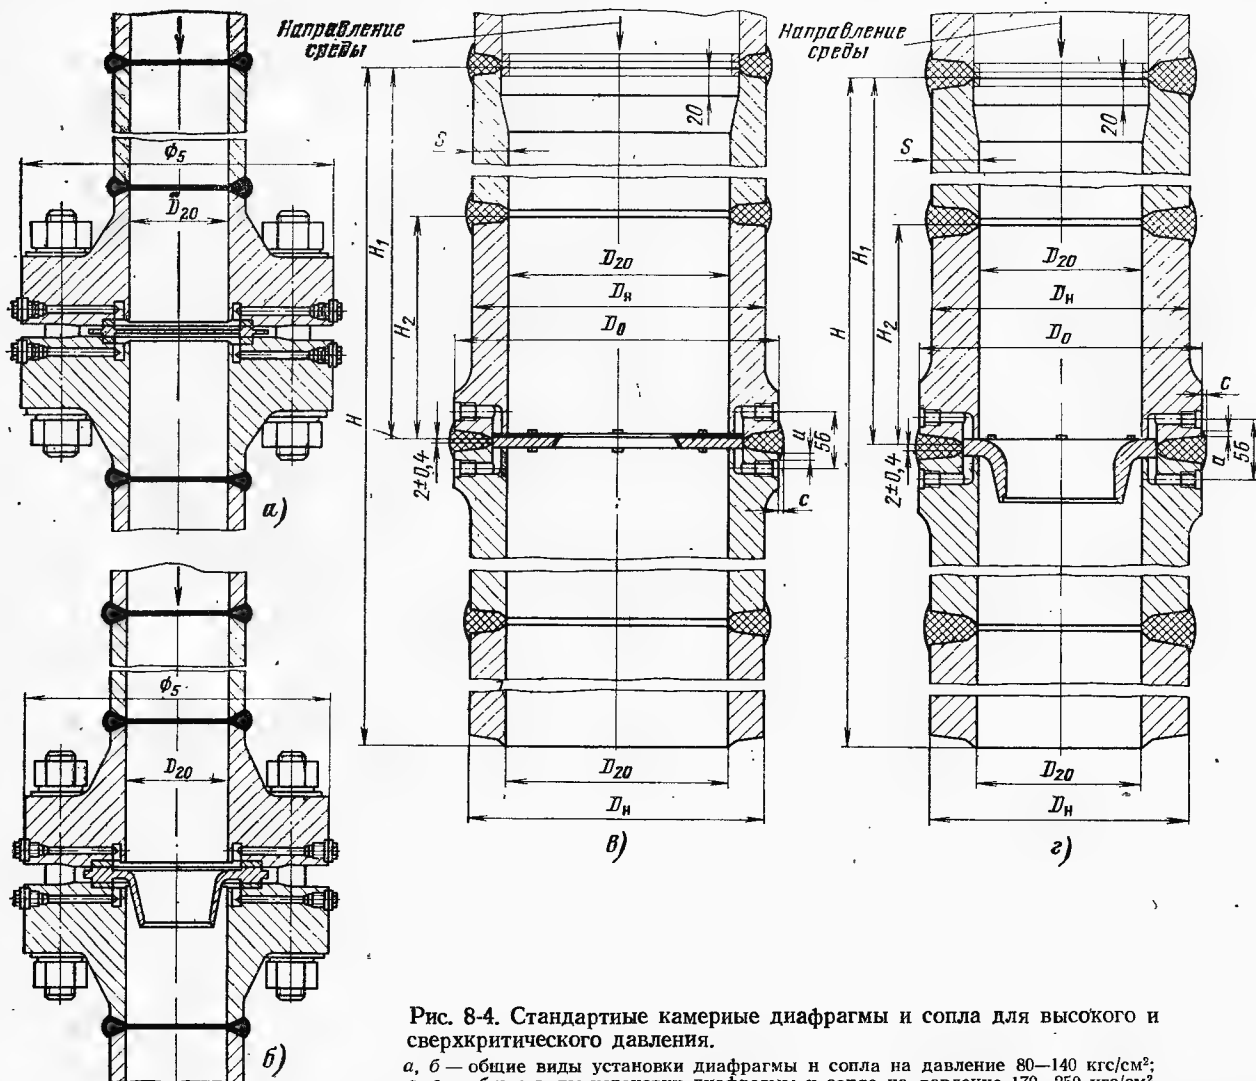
Стандартные камерные диафрагмы и сопла для высокого и сверхкритического давления.
